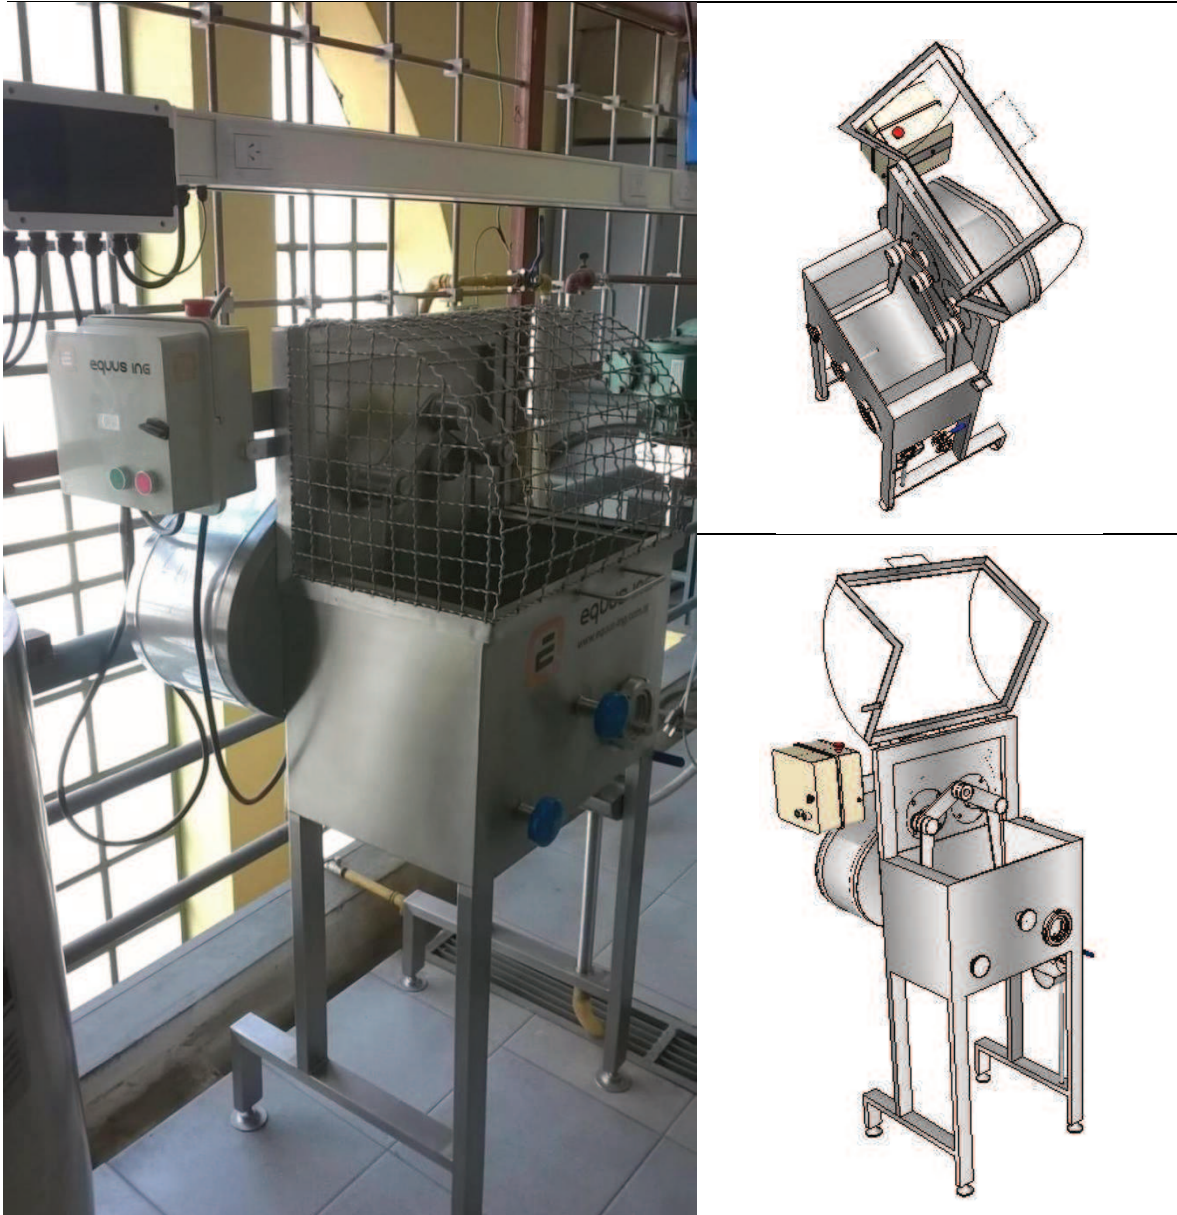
Hiladora diseñada para la planta piloto del INLAIN.
